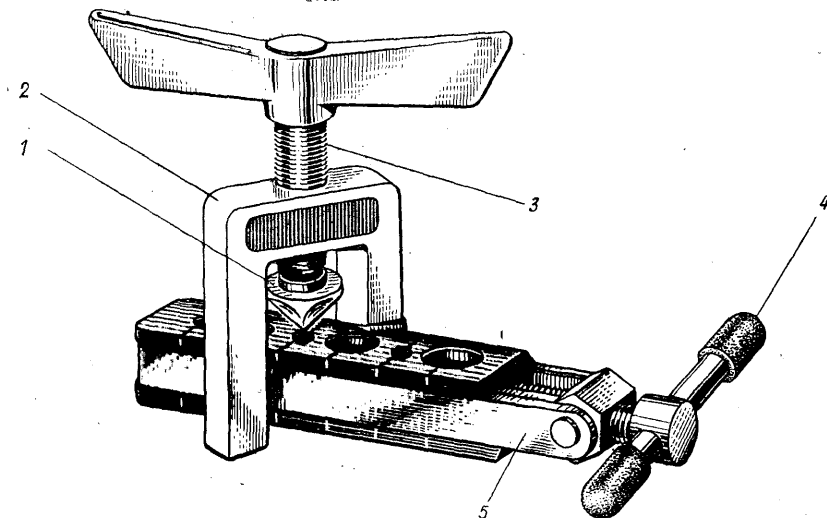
Приспособление для разбортовки труб с помощью конусного пуансона:
